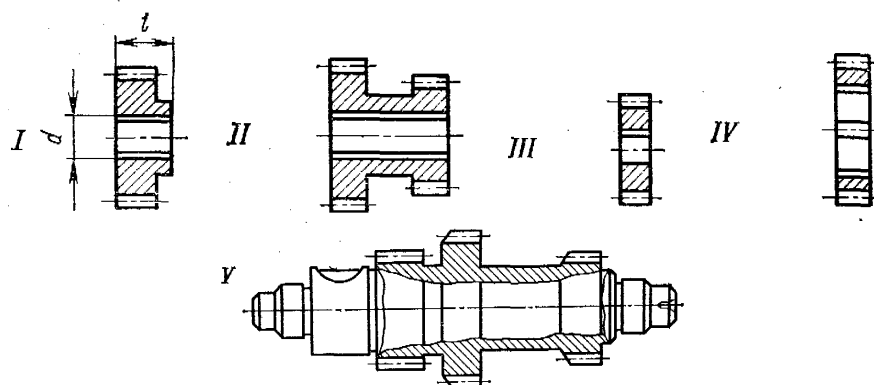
Типы цилиндрических зубчатых колес
